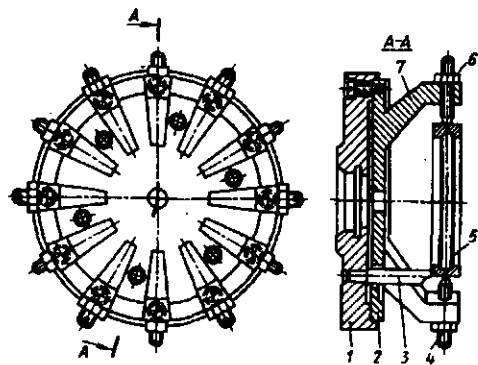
Мембранный патрон с винтовым центрированием обрабатываемой детали: 1 – планшайба; 2 – мембрана; 3 – упоры; 4 – винты; 5 – обрабатываемая деталь; 6 – гайка; 7 – кулачки
